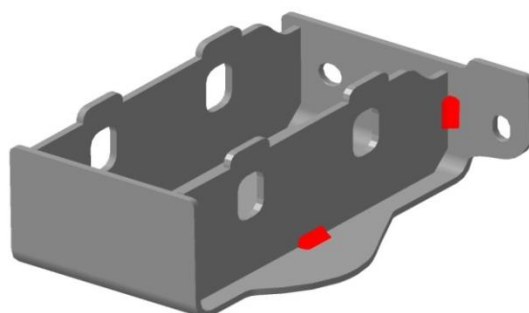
Первый этап сборки-сварки крепежного узла
